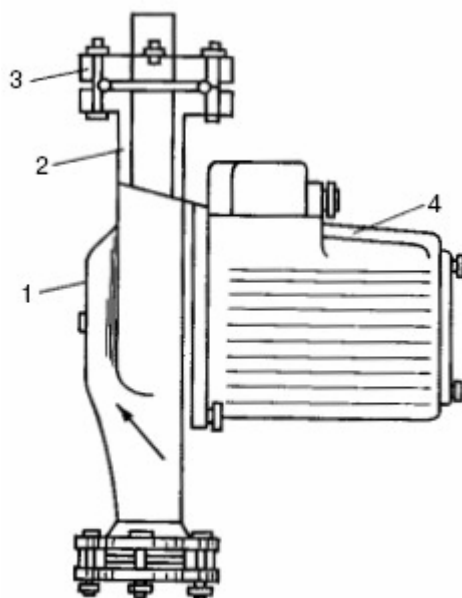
Диагональный насос ЦВЦ: 1 – корпус; 2 – нагнетательный патрубок; 3 – контрфланец для присоединения трубы; 4 – электродвигатель
